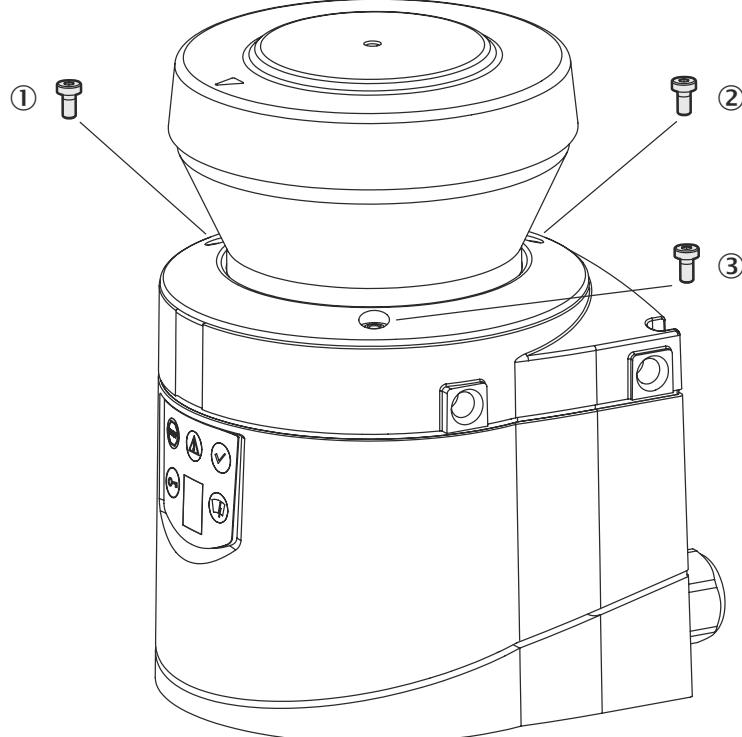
Befestigungsschrauben der Optikhaube lösen
